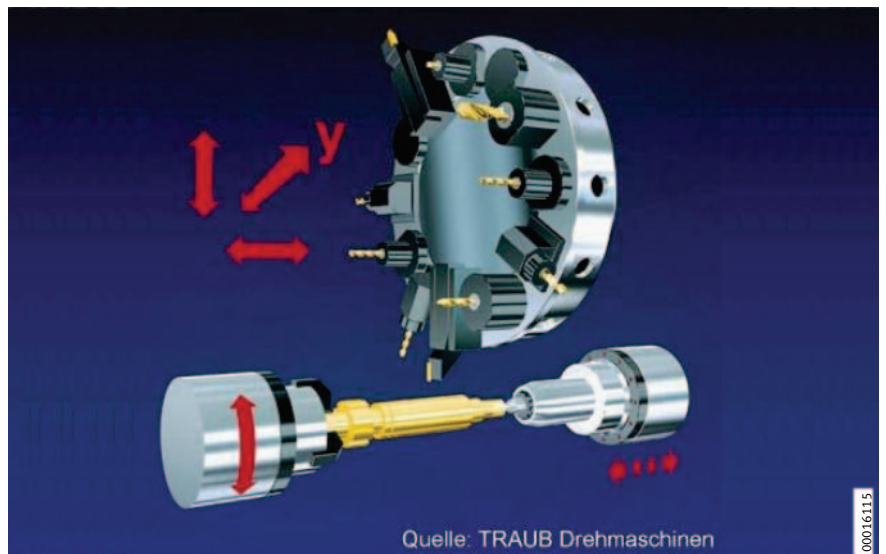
Werkzeugträger mit angetriebenen Werkzeugen
